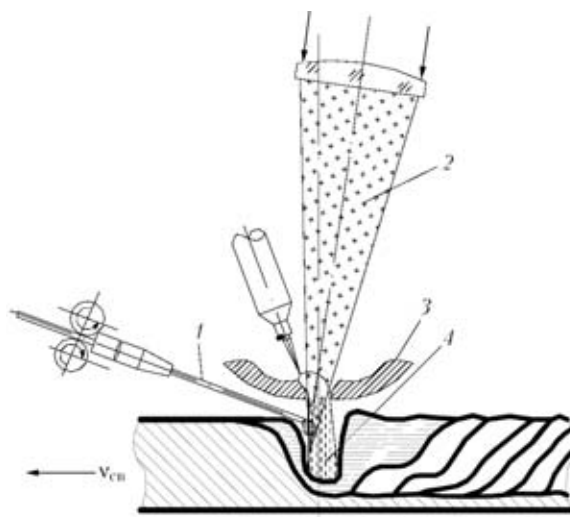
Схема гибридной лазерно-плазменной сварки: 1 — присадочная проволока; 2 — лазерный пучок; 3 — сопло плазмотрона; 4 — плазменная дуга
